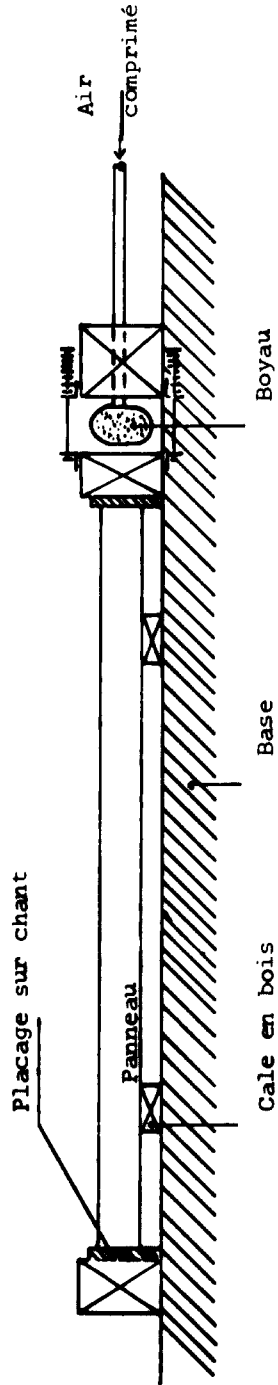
FIGURE XXII. PRINCIPE D'UNE MACHINE AUTOMATIQUE A PLAQUER AVEC DISPOSITIFS COMPLEMENTAIRES (VUE DE DESSUS). LA MACHINE EMPLOIE DE LA COLLE THERMOPLASTIQUE
